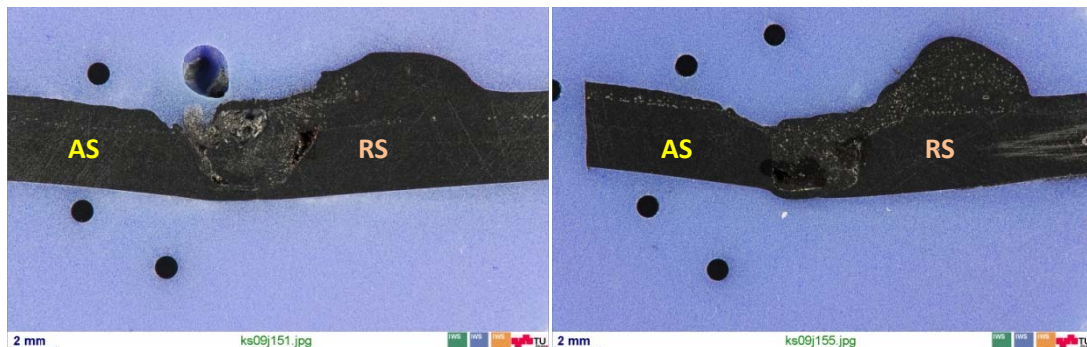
Ultradur-Makroschliff konventionelle FSW-Werkzeuge: WKZ 2 (links) und WKZ 3 (rechts)
